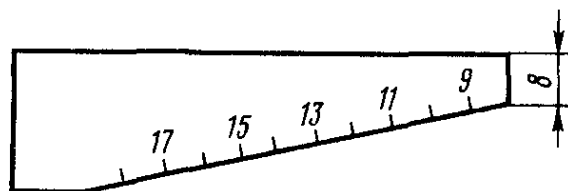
Шаблон для замера разрыва и провала контактов переключателя ТК-8, реверсора РК-8 и разрыва контактов контактора МКП-23
